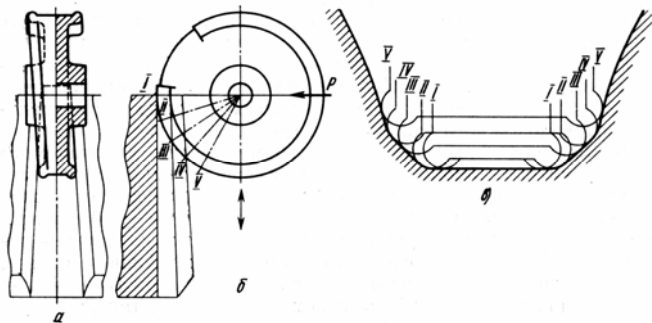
Устройство для поперечного обкатывания зубчатого колеса бортовой передачи экскаватора на токарном станке
